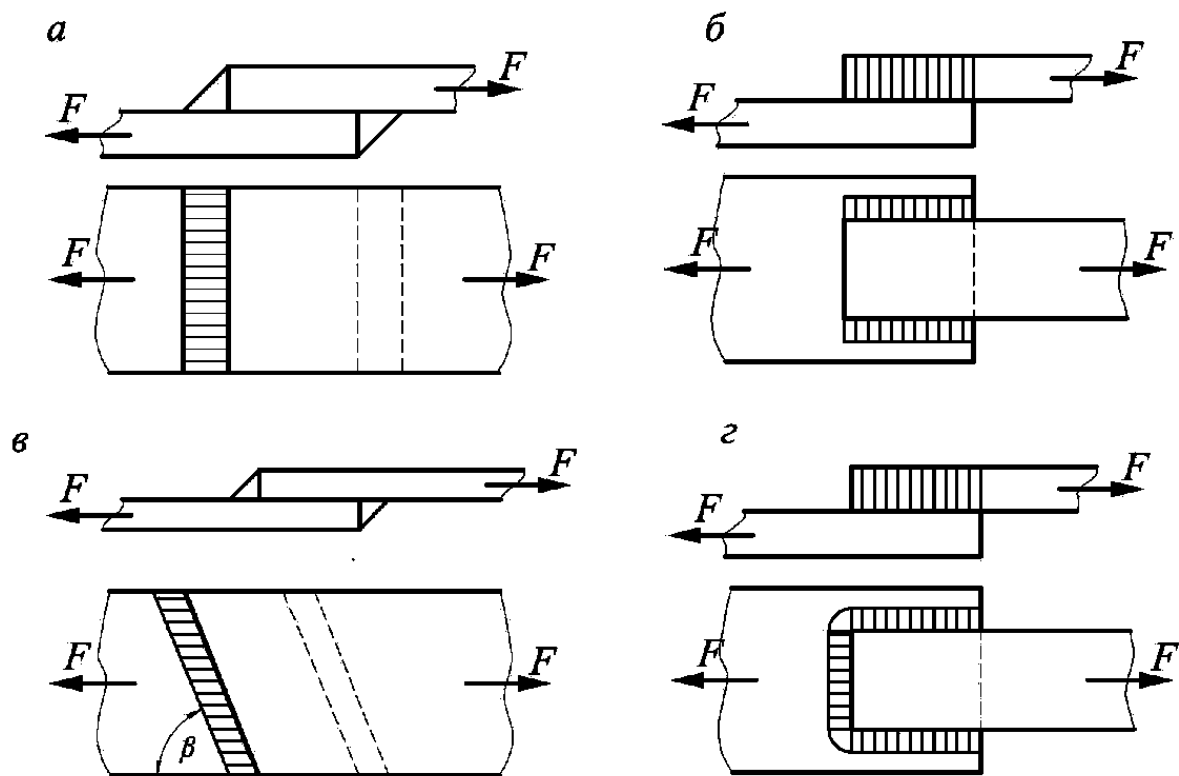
Угловые сварные швы нахлесточных соединений
